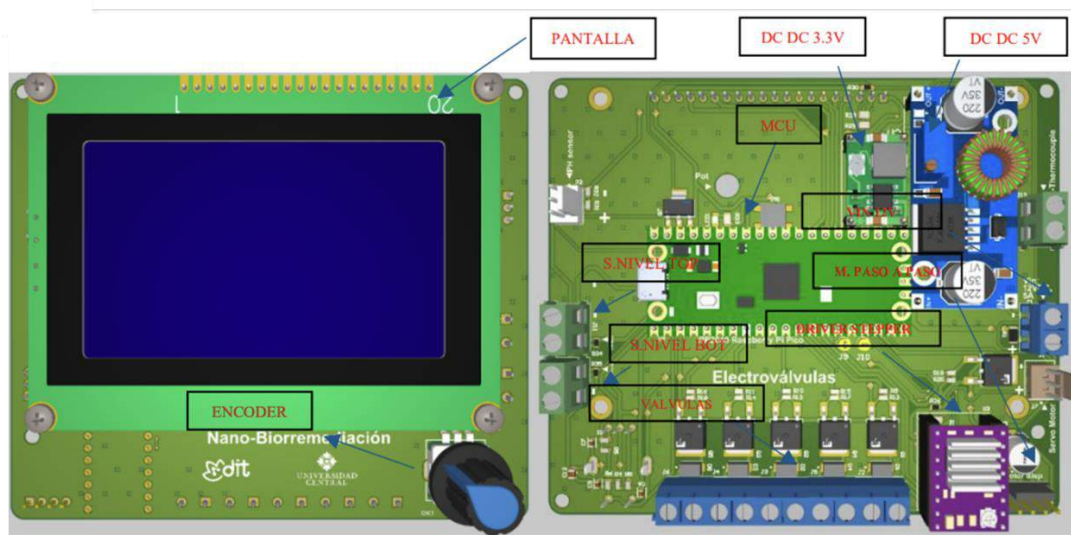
Visualización de la PCB del módulo de control. A) Frontal, B) Trasera
